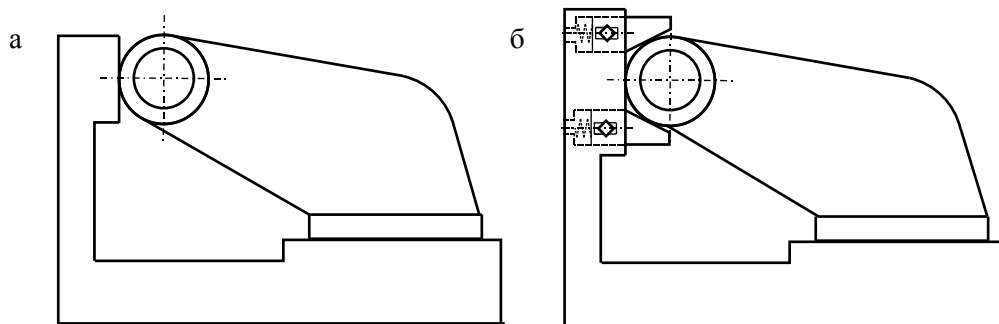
Установка детали по плоской и цилиндрической поверхности
